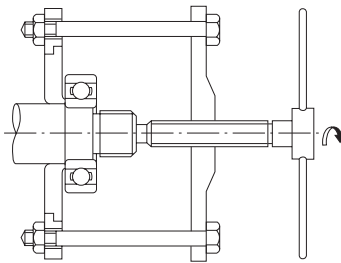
Demontage des Innenrings mit Abziehwerkzeug (1)
